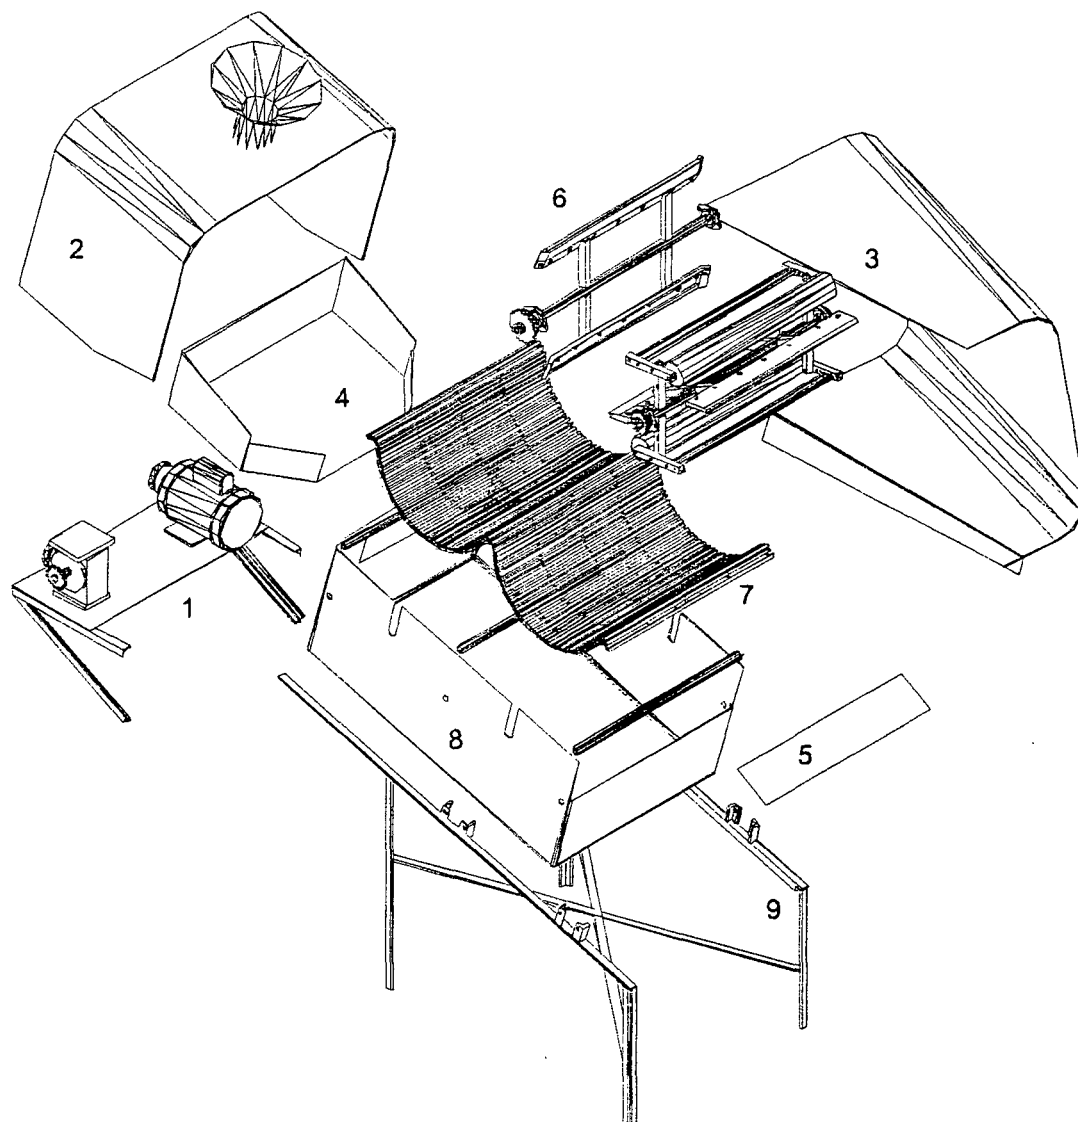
Ilustração das partes componentes do separador modificado (protótipo definitivo): 1 - conjunto motor-redutor e sua estrutura; 2 - chapa de proteção com funil; 3 - chapa de proteção basculante; 4 - chapa de entrada de material; 5 - chapa de saída de sólidos; 6 - conjunto raspador e roletes; 7 - peneira perfilada; 8 - chapas de suporte da peneira; 9 - estrutura do equipamento.
